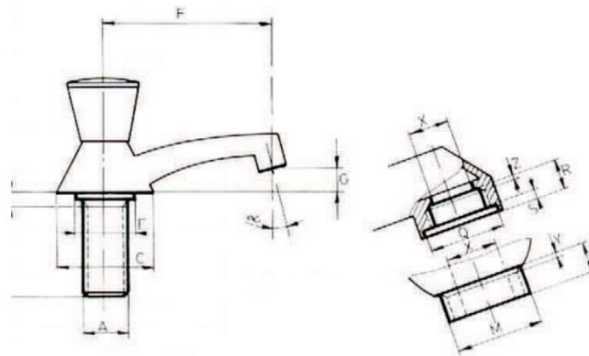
Dimensiones a tener en cuenta en el diseño del grifo
